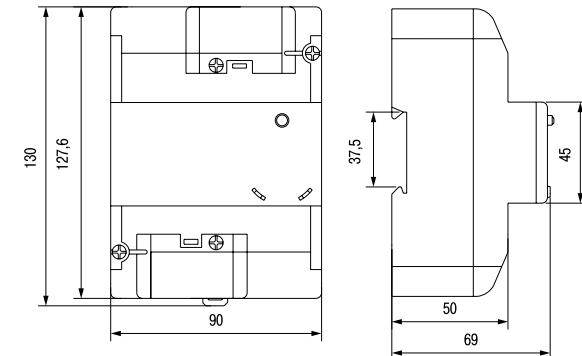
Габаритные и присоединительные размеры счётчиков габарита корпуса 1
